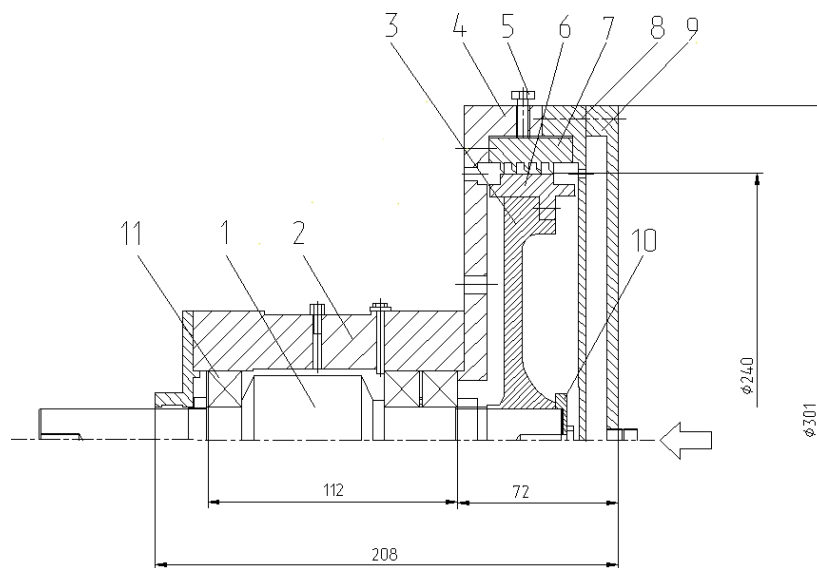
Поперечное сечение испытательной головки стенда: 1 – вал; 2 – блок подшипников; 3 – диск; 4 – корпус; 5 – регулировочный болт; 6 – роторная часть уплотнения; 7 – статорная часть уплотнения; 8 – передний фланец; 9 – задний фланец; 10 – фиксирующая шайба; 11 – подшипник
